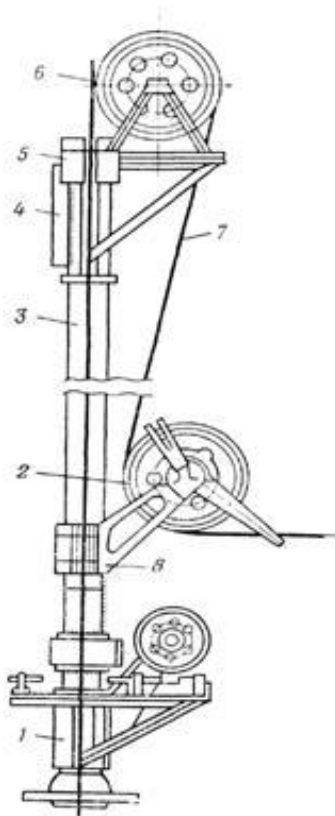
Общий вид лубризатора Л-4: 1 – основание; 2 – мерный ролик; 3 – приемная камера; 4 – кронштейн; 5 – сальник; 6 – верхний ролик; 7 – кабель; 8 – червячное колесо с кронштейном для установки приемной камеры
